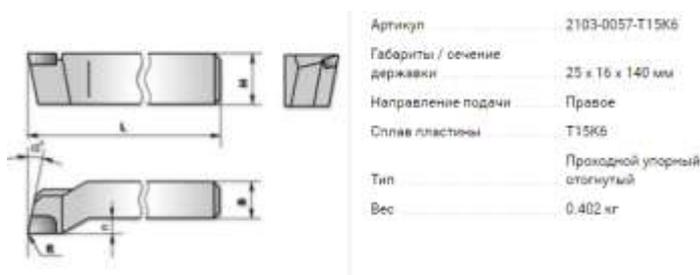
Внешний вид резца проходного упорного отогнутого
